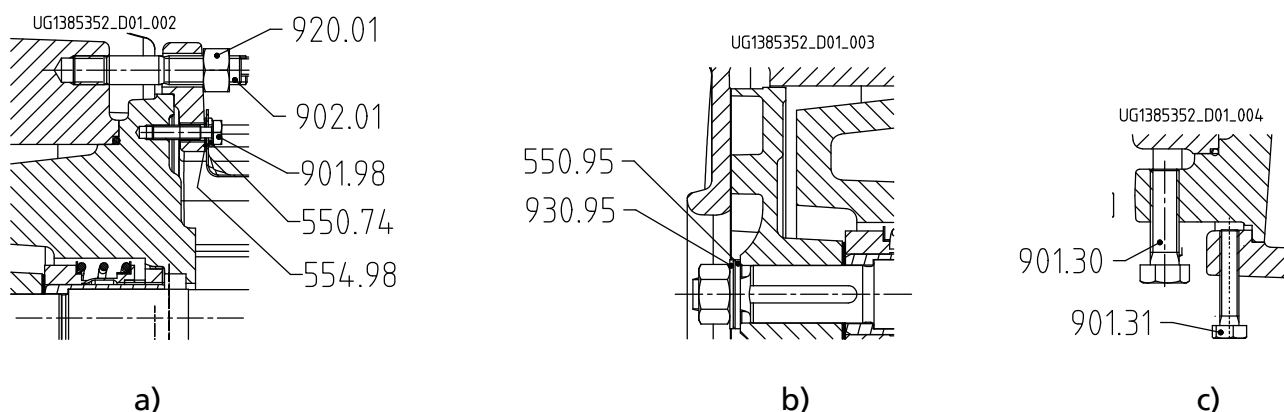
а) Зажимная крышка корпуса, б) Крепление рабочего колеса при WE 25, в) Расположение отжимных винтов
